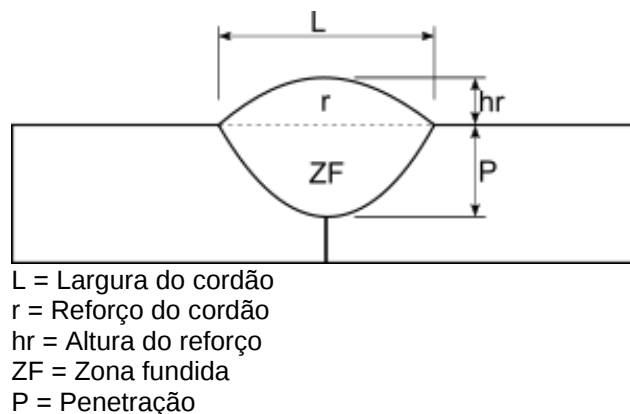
Desenho representativo de um corpo de prova em corte transversal com a indicação das dimensões utilizadas para análise do perfil geométrico do cordão de solda.
